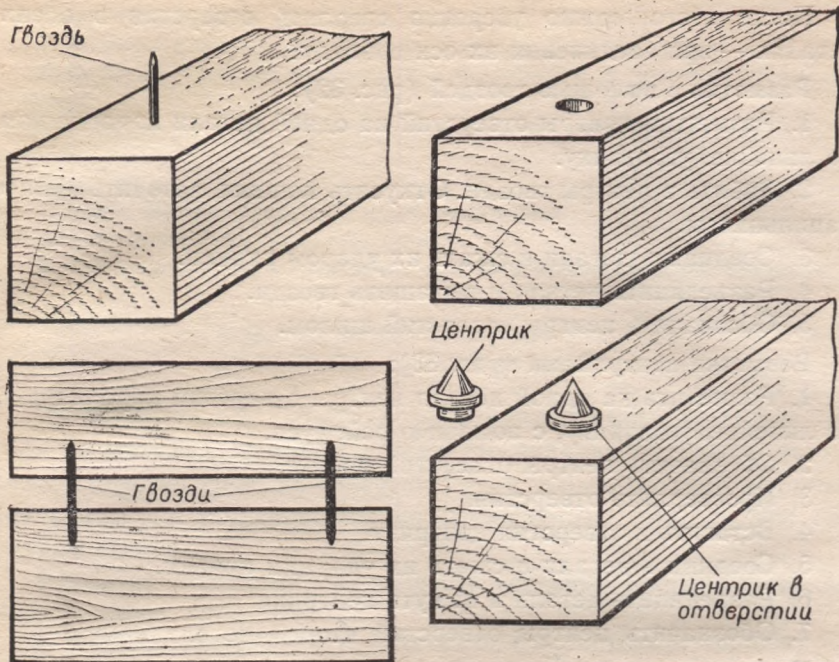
Разметка отверстий под круглые шипы гвоздиками.
